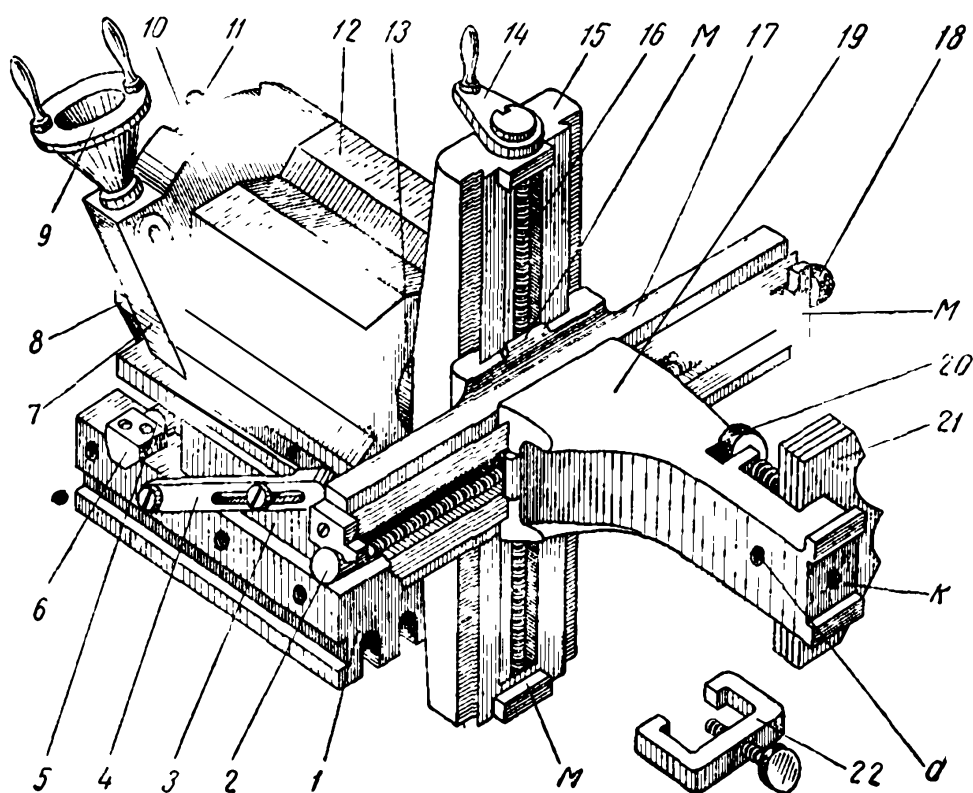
Универсальное приспособление для координатного шлифования конструкции Адрианова.
